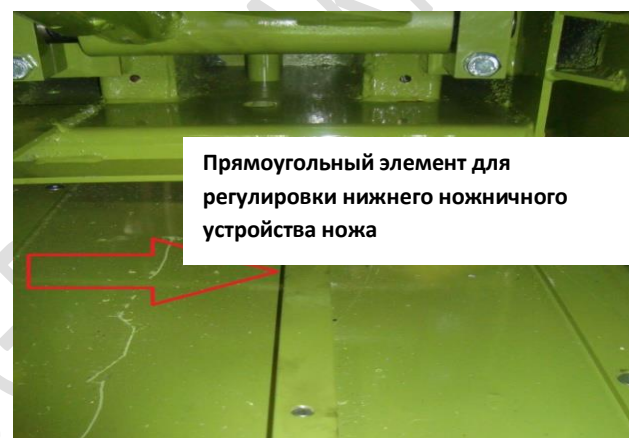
Регулировочная пластина нижнего ножничного устройства ножа
